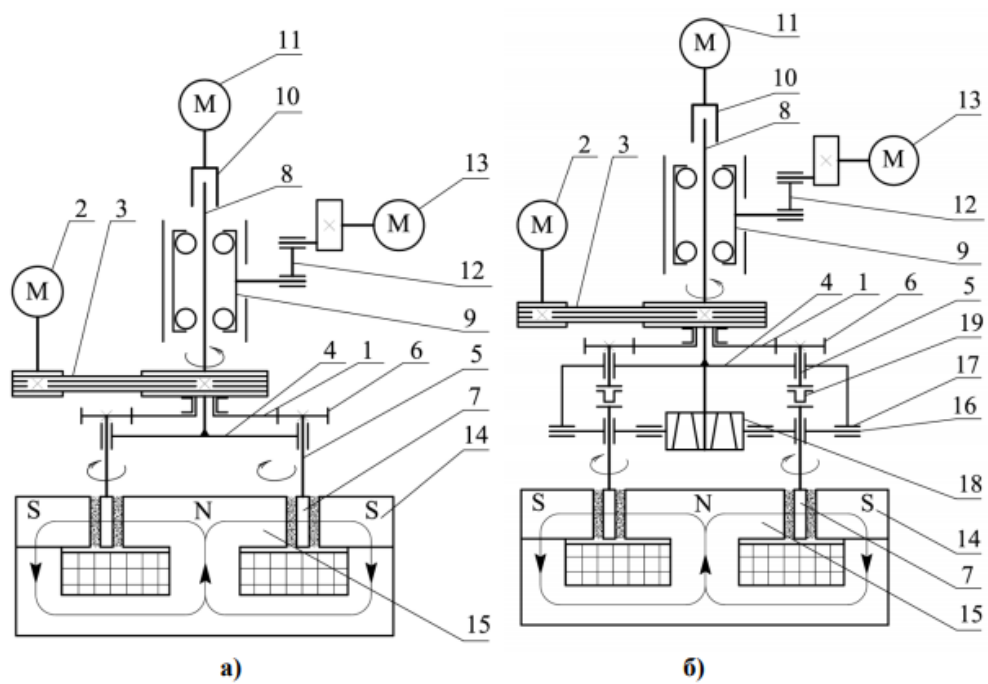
Схема оброблення деталей в обертовій кільцевій ванні:
